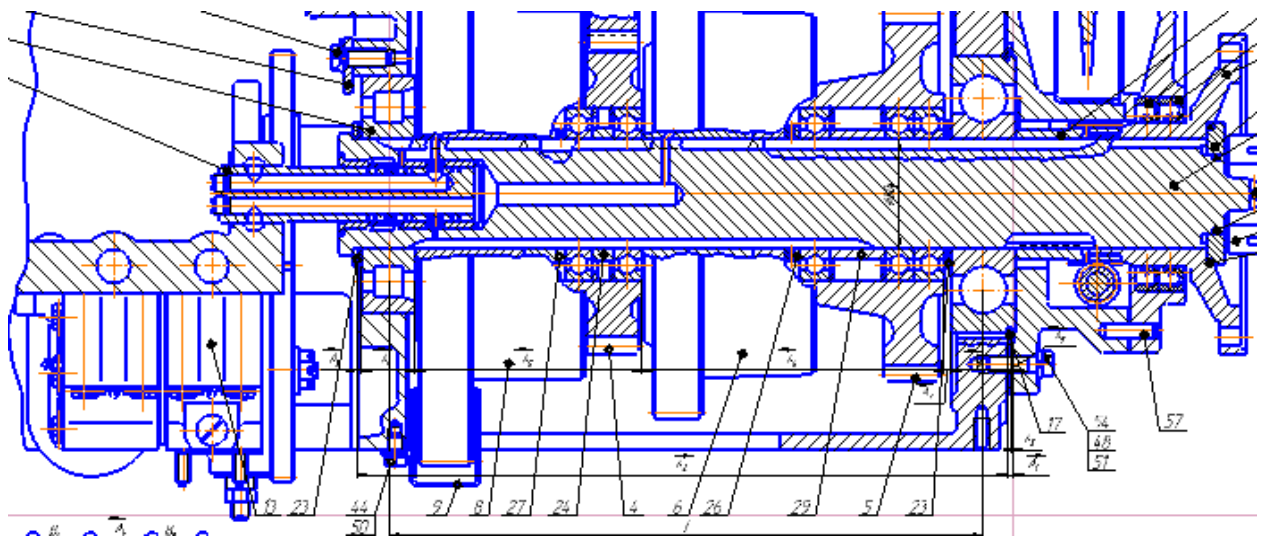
Фрагмент коробки передач з тормозом уповільнювачем
